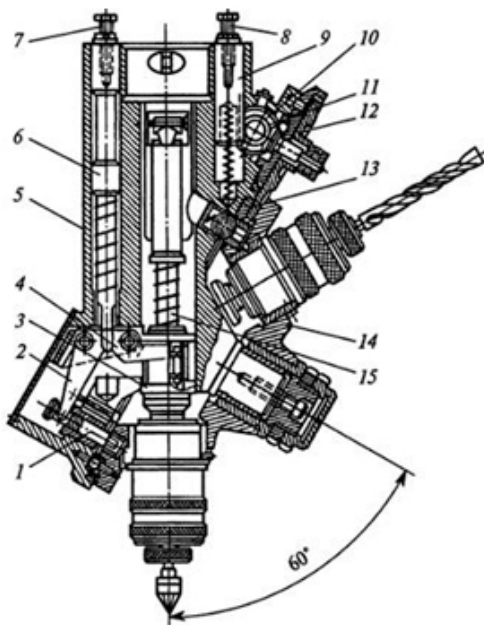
Шестишпиндельная револьверная головка: 1 – фиксатор; 2 – рычаг фиксатора; 3 – ведущая полумуфта; 4 – рычаг муфты; 5 – корпус основной; 6 – стержень; 7, 8 – упорные винты; 9 – рейка; 10 – зубчатое колесо; 11 – коническая зубчатая передача; 12 – храповой механизм; 13 – зубчатый вене; 14 – поворотный корпус; 15 – шпиндель головки
